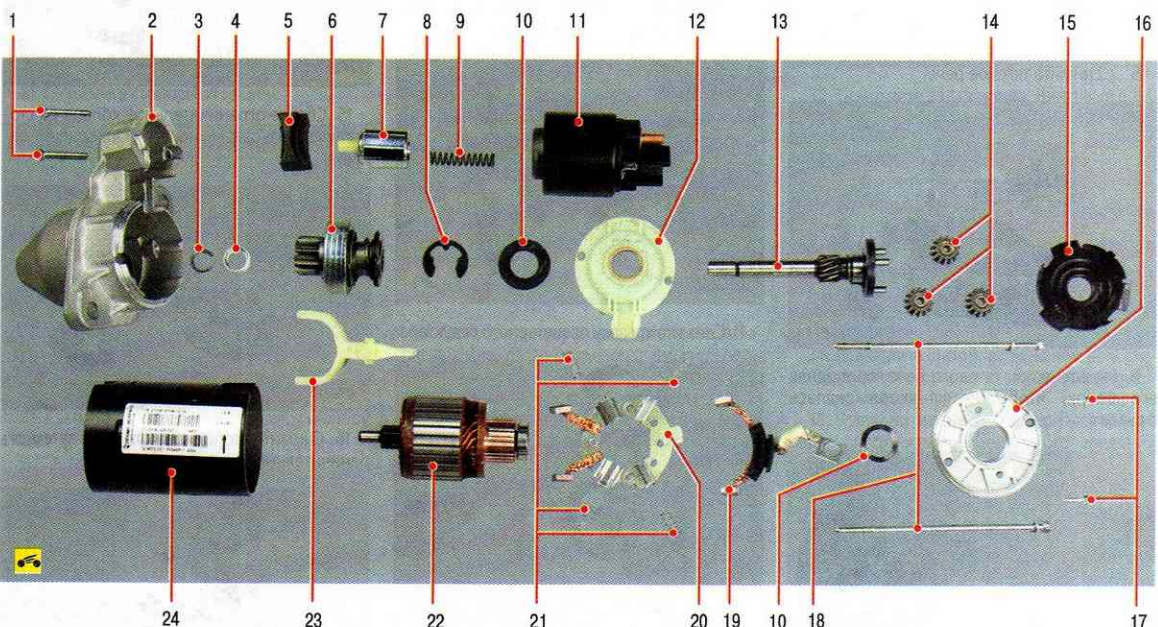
Детали стартера 2110-3708010-02: 1 – винты крепления тягового реле; 2 – передняя крышка; 3 – стопорное кольцо; 4 – ограничительное кольцо; 5 – опора рычага; 6 – муфта свободного хода привода стартера; 7 – якорь реле; 8 – стопорная шайба; 9 – возвратная пружина; 10 – дистанционная шайба; 11 – тяговое реле; 12 – опора вала привода; 13 – вал привода; 14 – планетарные шестерни (сателлиты); 15 – крышка планетарного редуктора; 16 – задняя крышка; 17 – винты крепления щеткодержателя; 18 – стяжные болты; 19 – соединительная шина с изолированными щетками; 20 – щеткодержатель с «отрицательными» щетками; 21 – прижимные пружины; 22 – якорь; 23 – рычаг привода; 24 – корпус
